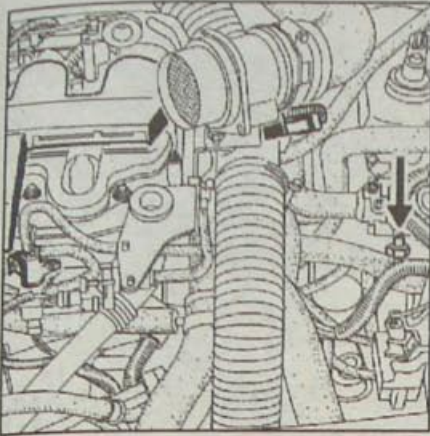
Расположение гайки крепления штока левой подвески двигателя
